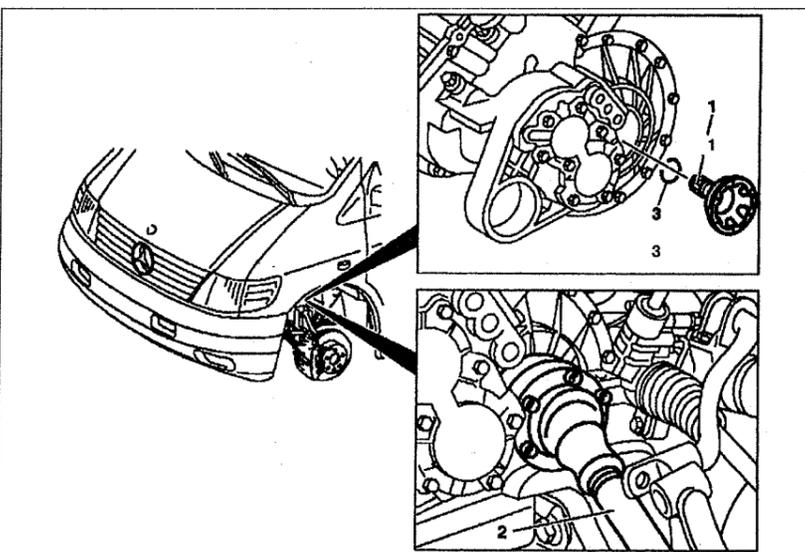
Левый фланец коробки передач: 1. Фланец, 2. Полуось, 3. Стопорное кольцо.
